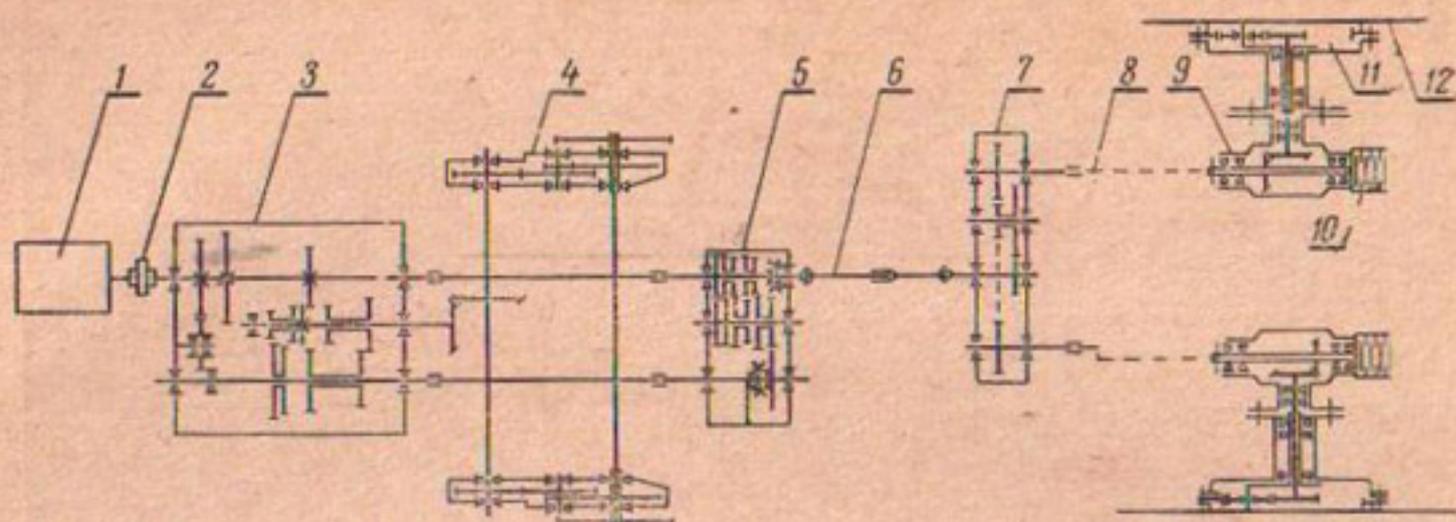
Кинематическая схема канавокопателя КФН-1200:
